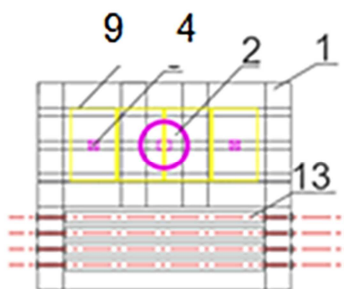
Общий вид пресса для изготовления брикетов (вид сверху).
